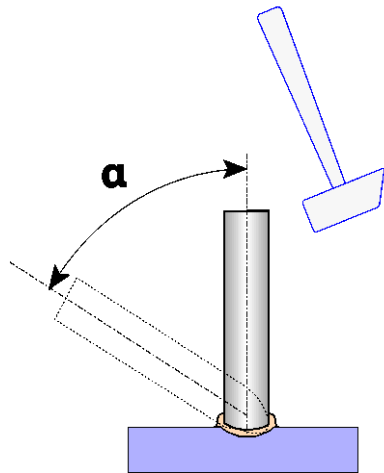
Sichtprüfung einer Bolzenschweißung
